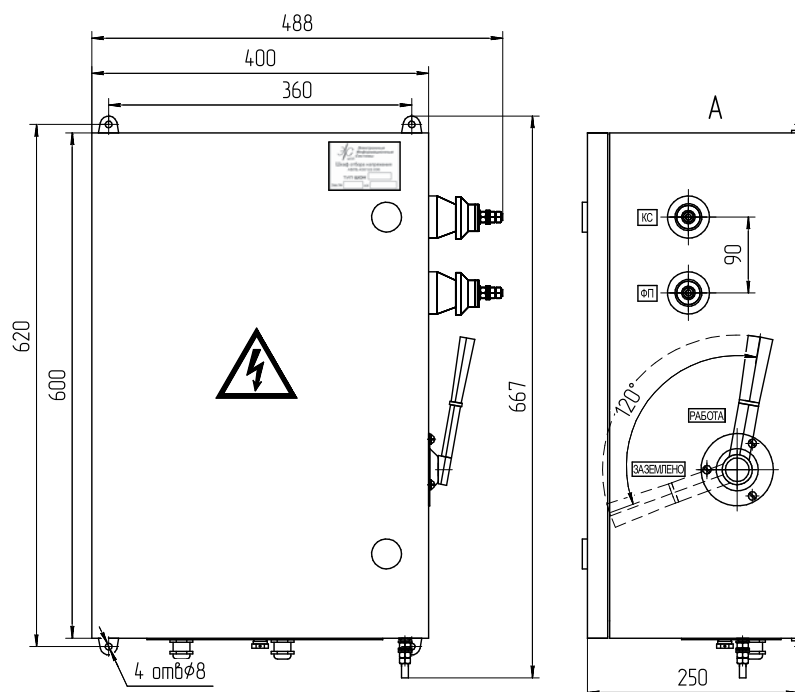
Габаритно-присоединительный чертеж ШОН-303П.
